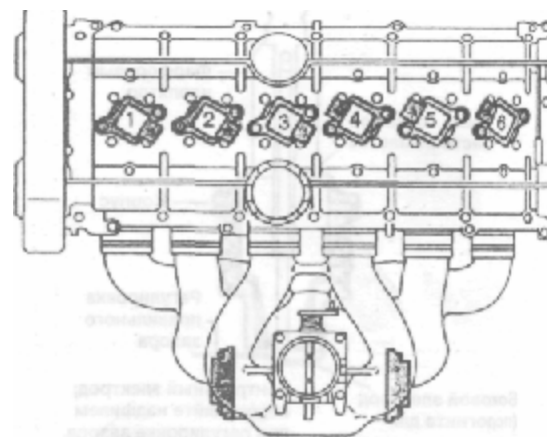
6-цилиндровый двигатель B6304F. Порядок работы цилиндров: 1-5-3-6-2-4.
